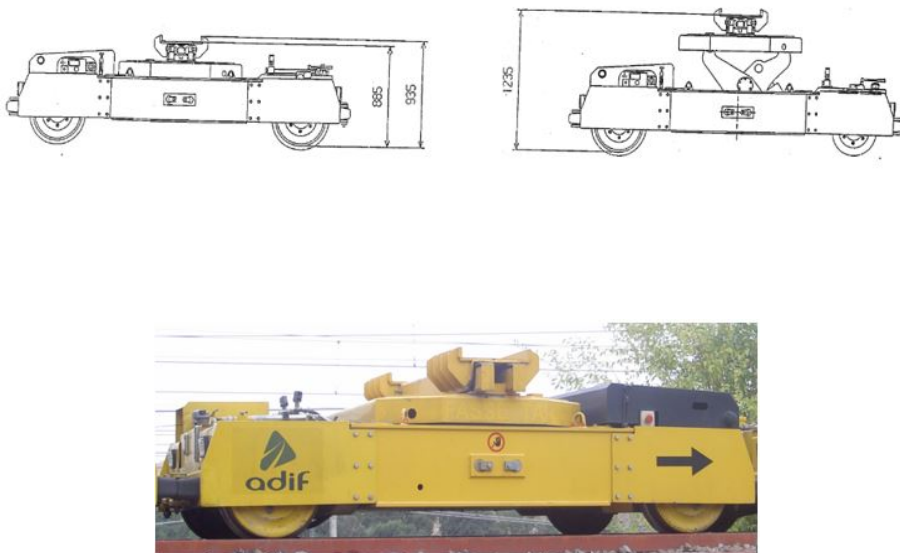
Sistema modular PEM/LEM. Detalles y vista general del carro elevador motorizado (LEM)
